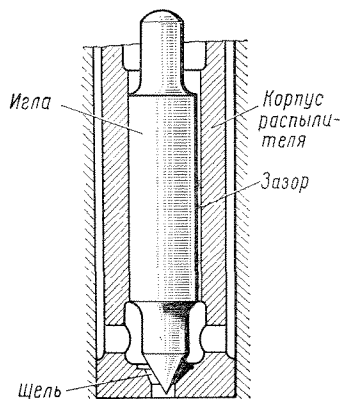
Несоосность расположения поверхности иглы и поверхности корпуса
